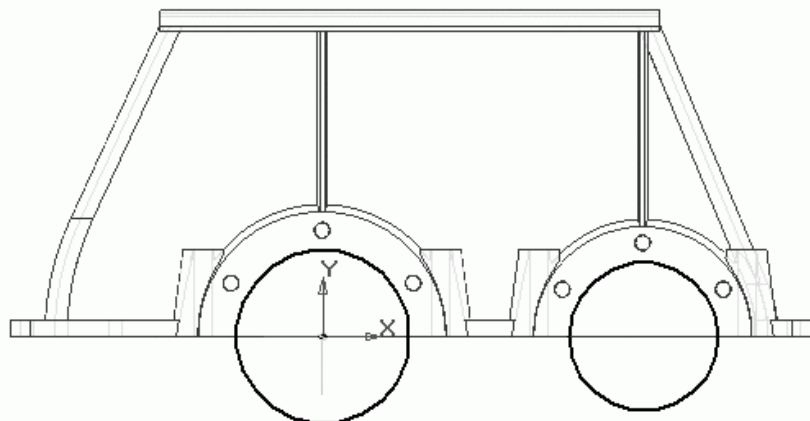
Эскиз отверстий под подшипники в корпусе
